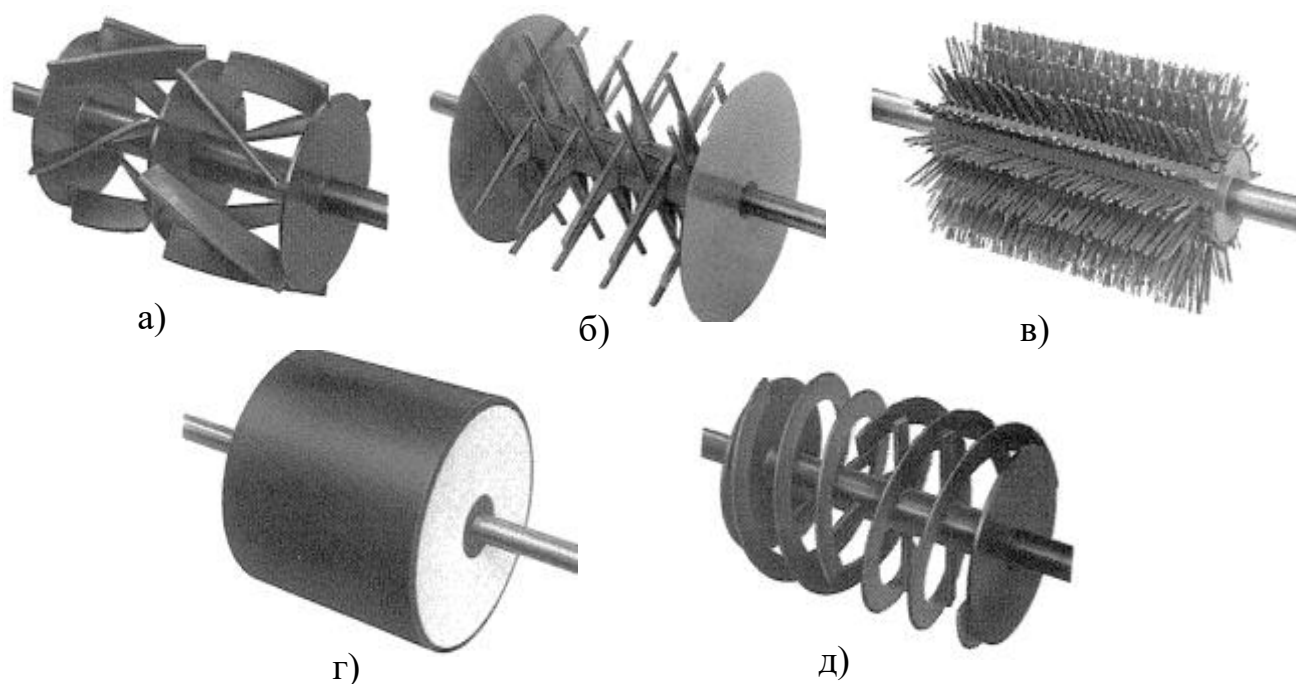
Типи роторів змішувача PEKAY Machine & Engineering Co., Inc [58]: а) лопатевий; б) голчастий; в) щітковий; г) суцільний; д) спіральний.
